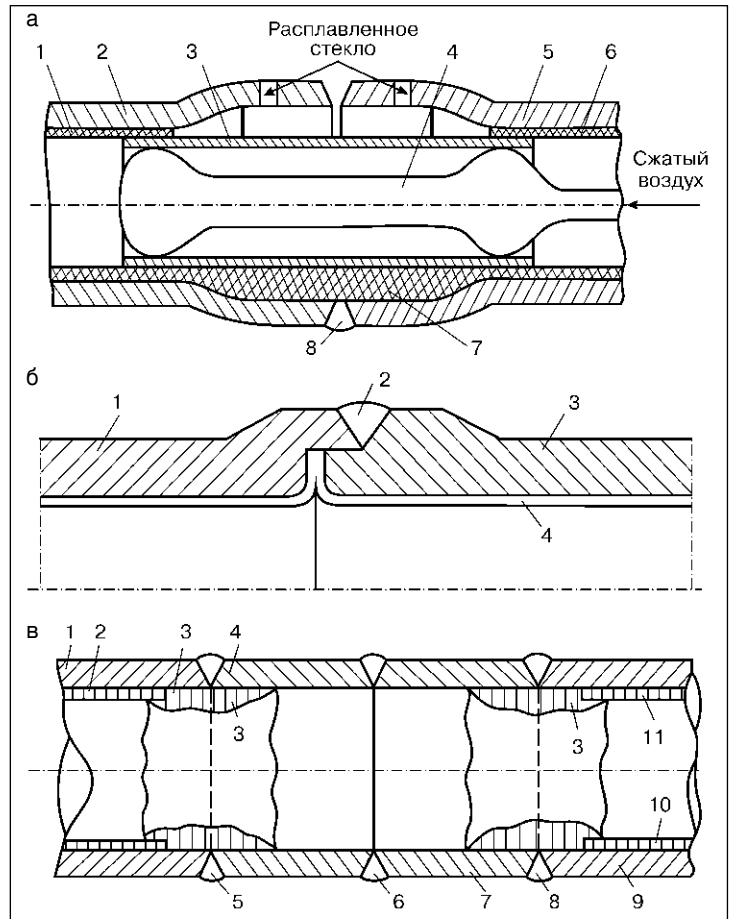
Конструктивные особенности соединения труб с внутренним защитным покрытием при использовании: а — формирующего устройства (1, 6 — эмалевое покрытие; 2, 5 — соединяемые элементы; 3 — эластичная трубка; 4 — камера; 7 — стеклоэмалевый расплав; 8 — сварной шов); б — замкового соединения (1, 3 — соединяемые трубы; 4 — защитное покрытие; 2 — сварной шов); в — промежуточных вставок (1, 9 — соединяемые трубы; 3, 10 — защитное покрытие; 4, 7 — трубные вставки из коррозионно-стойкого металла; 5, 8 — сварные швы)
